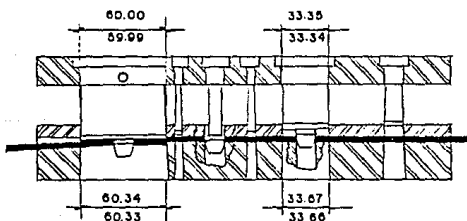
DISEÑO DE LA TIRA DE MATERIAL PARA LA PARTE MOSTRADA EN LA FIG. 9
